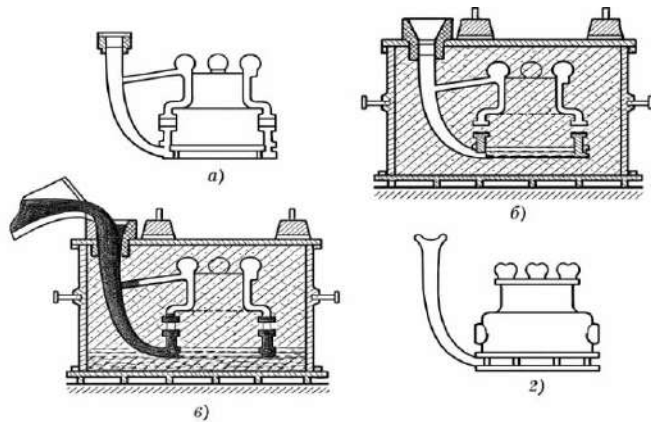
Схема виготовлення відливка по газифікованій моделі:
